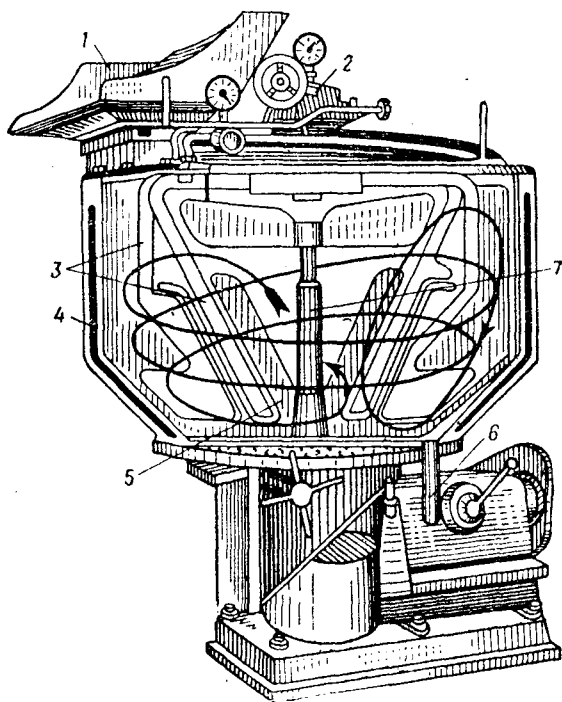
Центробежный (вихревой) смеситель для порошков и паст:
